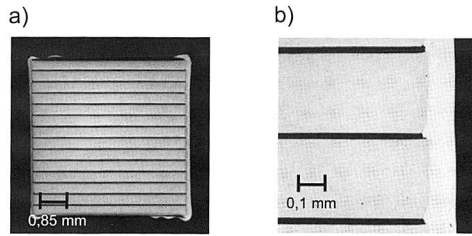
Schnittdansicht eines beidseitig beschichteten Ringkernblechpakets mit 14 Blechen; a) Gesamtansicht, b) Detailsicht
